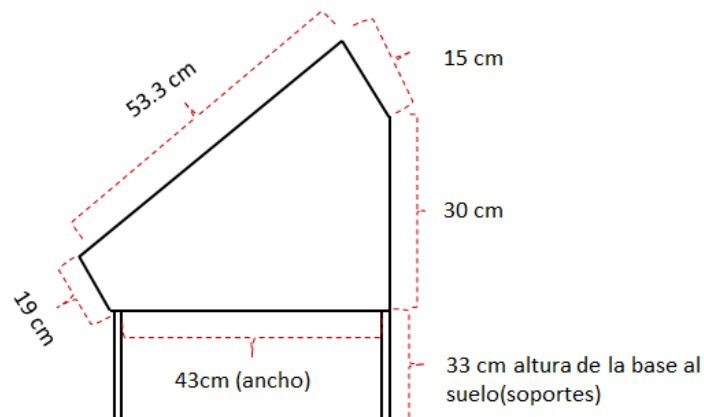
Dimensiones del deshidratador de 3kg parte lateral.
